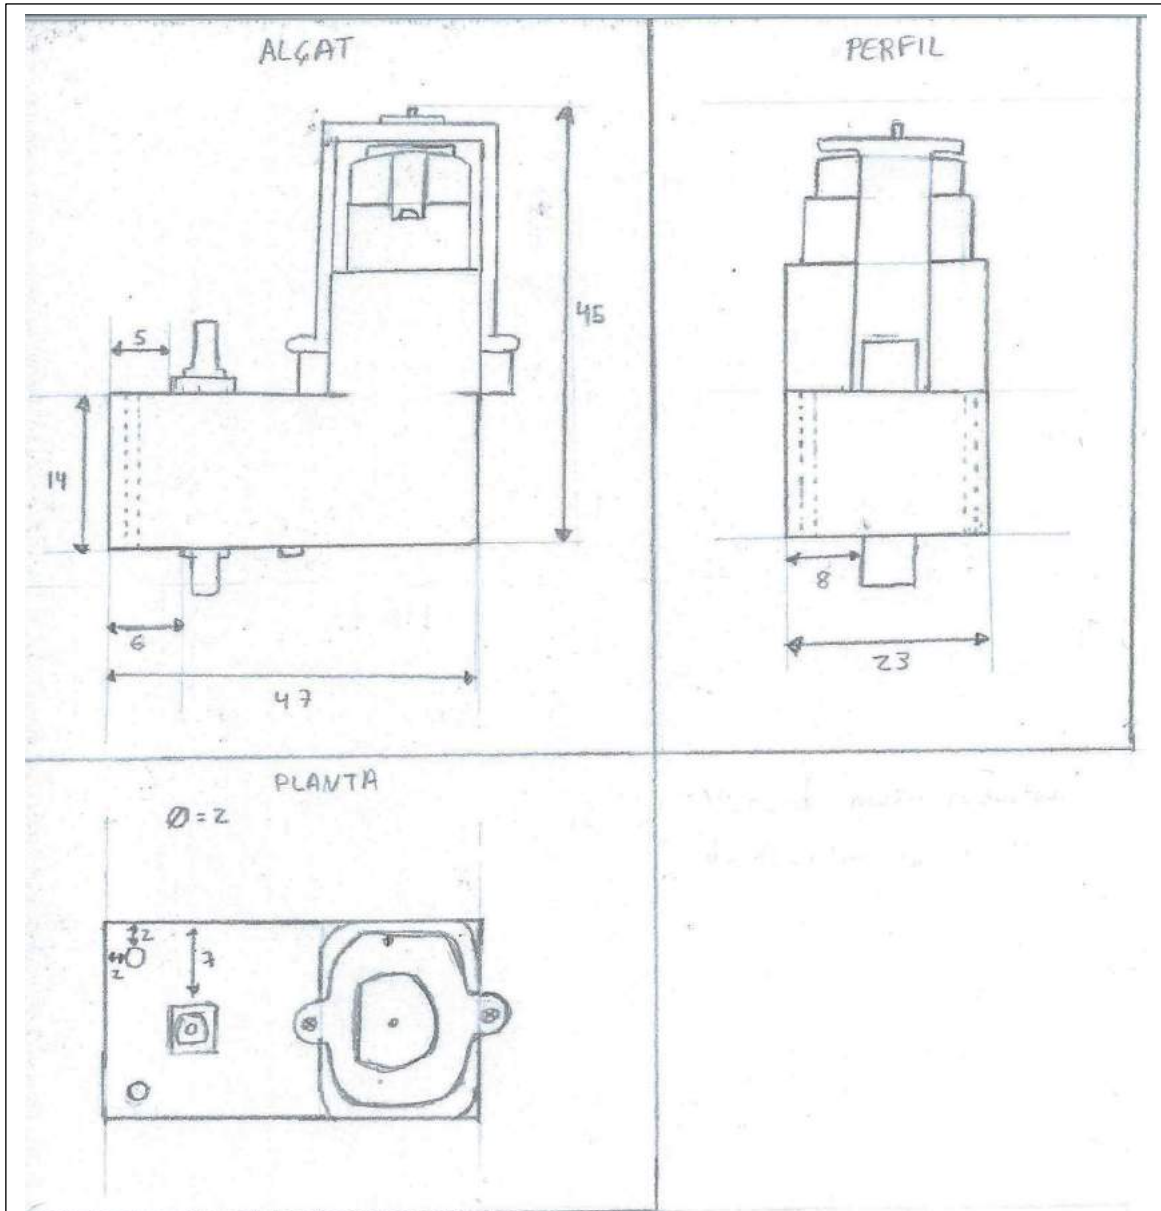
Vistes del motor reductor de 100 rpm colzar doble eix amb les mesures útils per fer la peça 3D. Les mesures estan en mil·límetres. Autor: Adrià Gironès.
